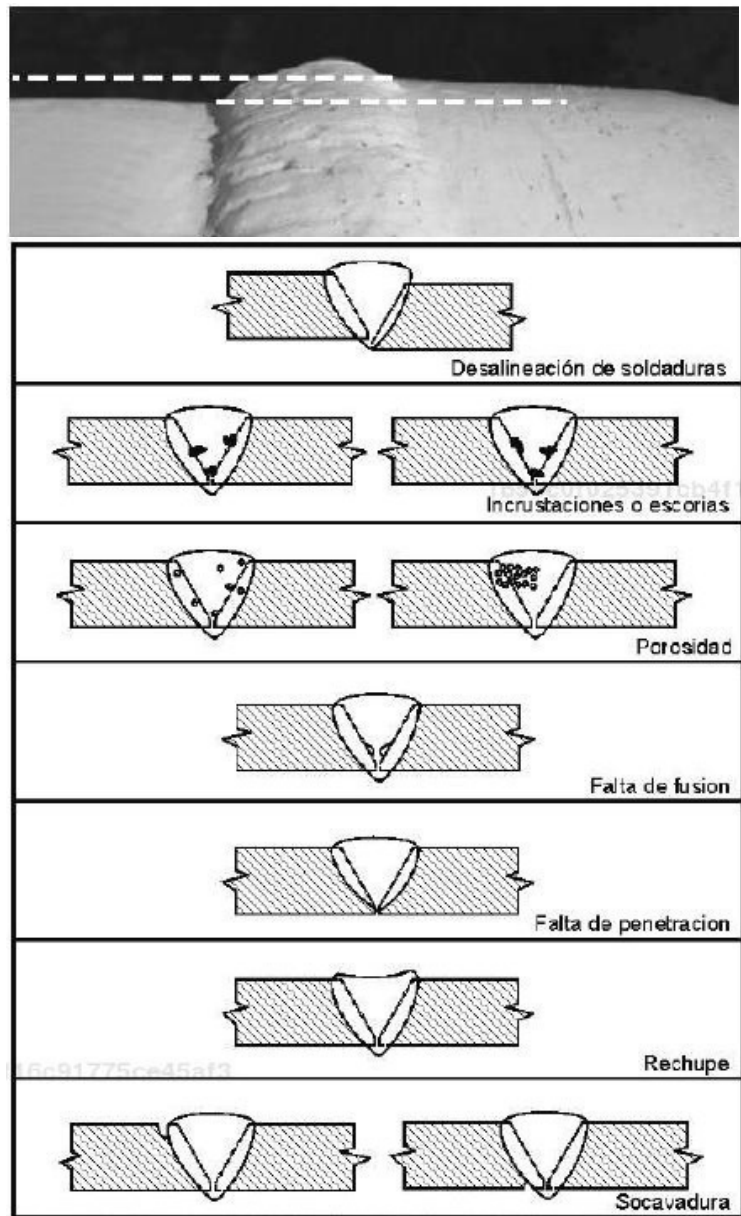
Discontinuidades en soldaduras [7]
